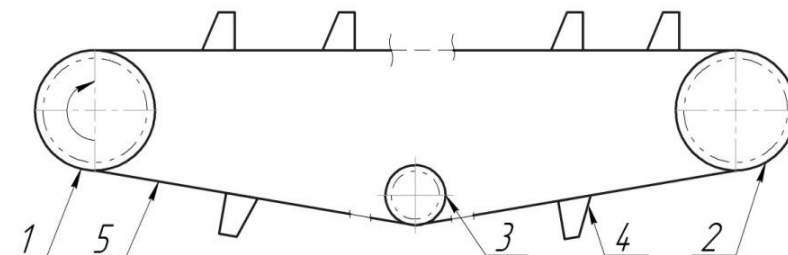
Схема режущего аппарата бесподпорного резания с поступательным движением режущих элементов: 1 – ведущая звездочка; 2 – ведомая звездочка; 3 – натяжитель; 4 – несущий элемент; 5 – цепь
